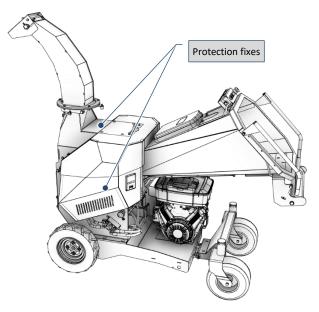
Protections fixes de la machine (vue côté gauche)
